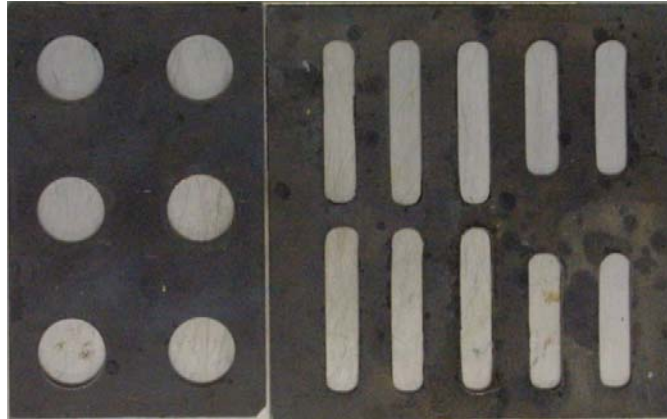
Moldes para probetas de 2 y 4 mm.
